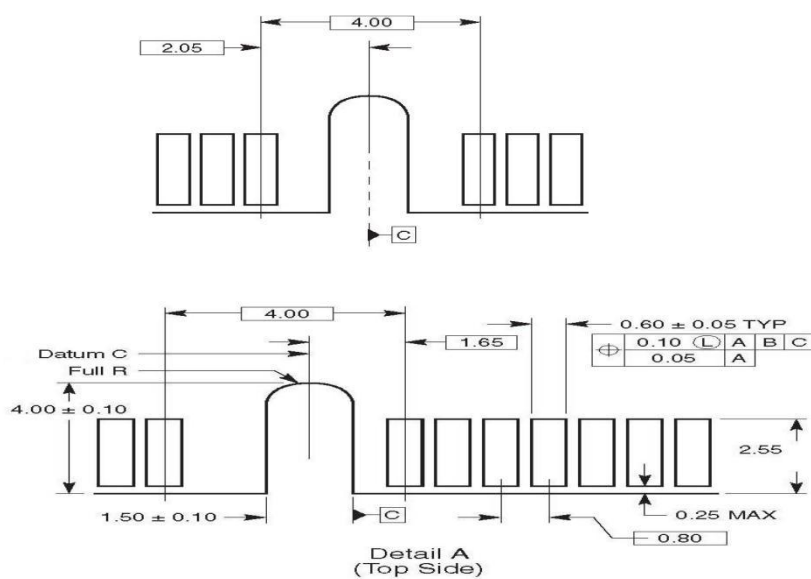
Mini PCIE Top 和 Bottom 细节尺寸
